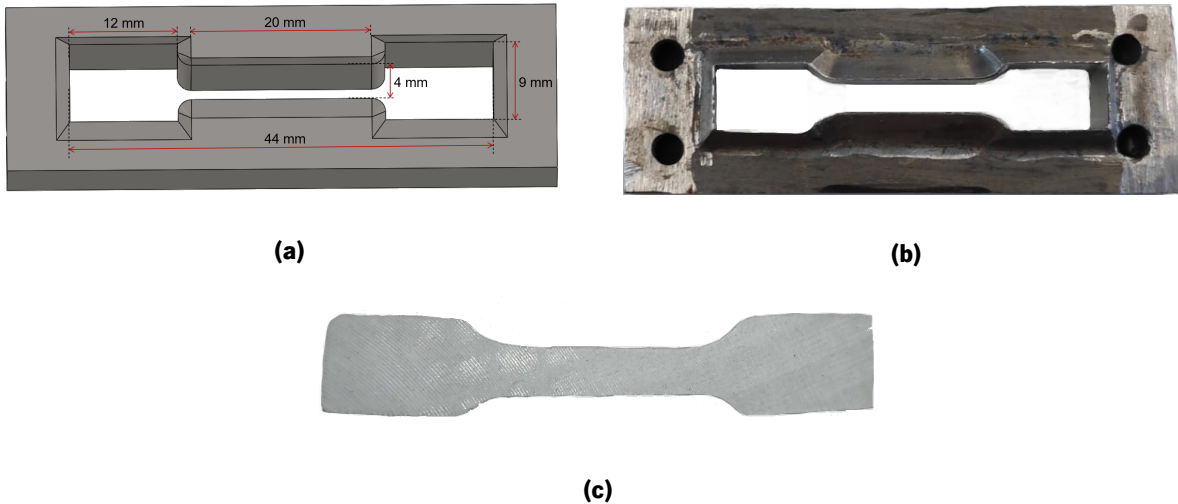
Provete utilizado nos ensaios de tração: a) dimensões do molde utilizado no corte dos provetes, b) imagem real do molde utilizado no corte dos provetes, c) imagem real de um provete utilizado.
